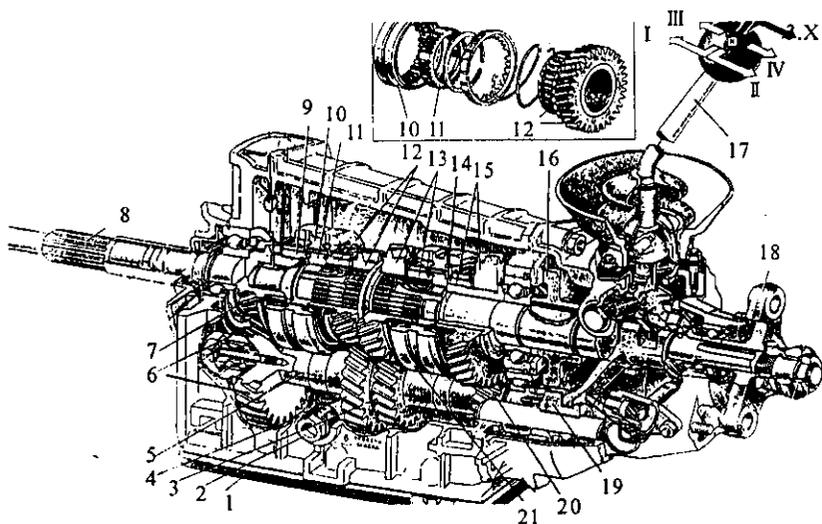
Устройство коробки передач автомобиля ВАЗ-2105:
